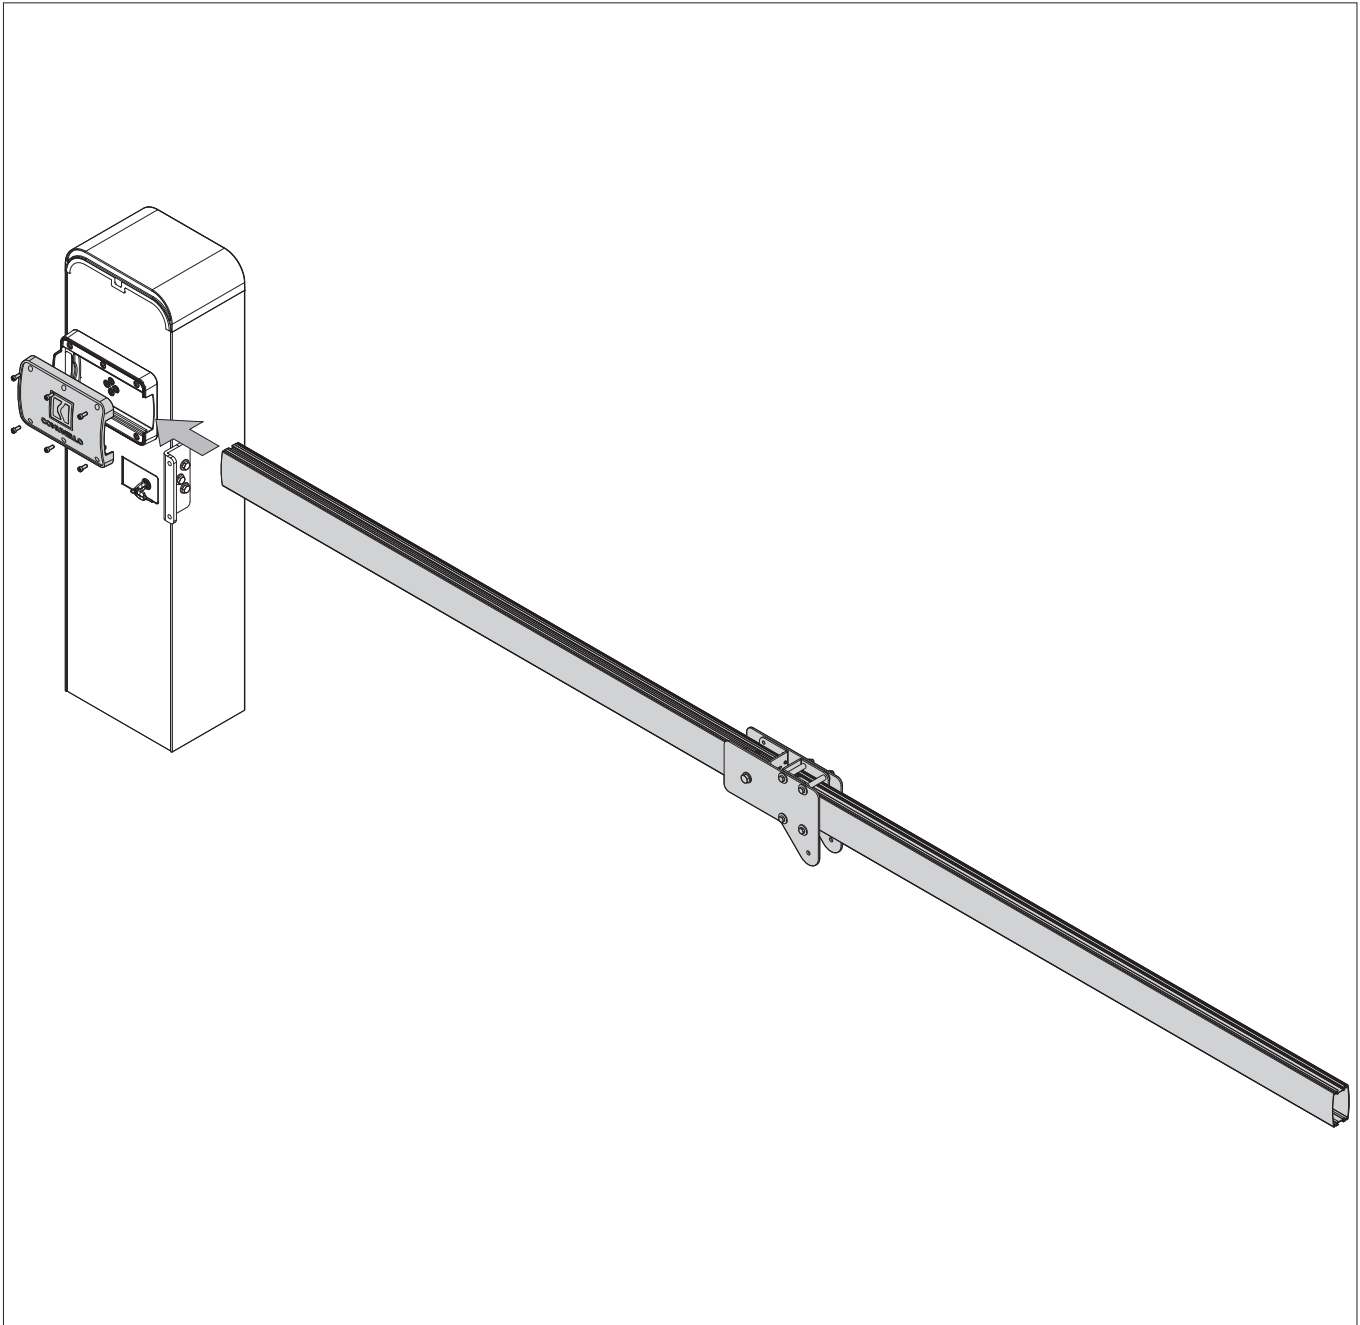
INSTALLAZIONE MEMBRO / ROD INSTALLATION
